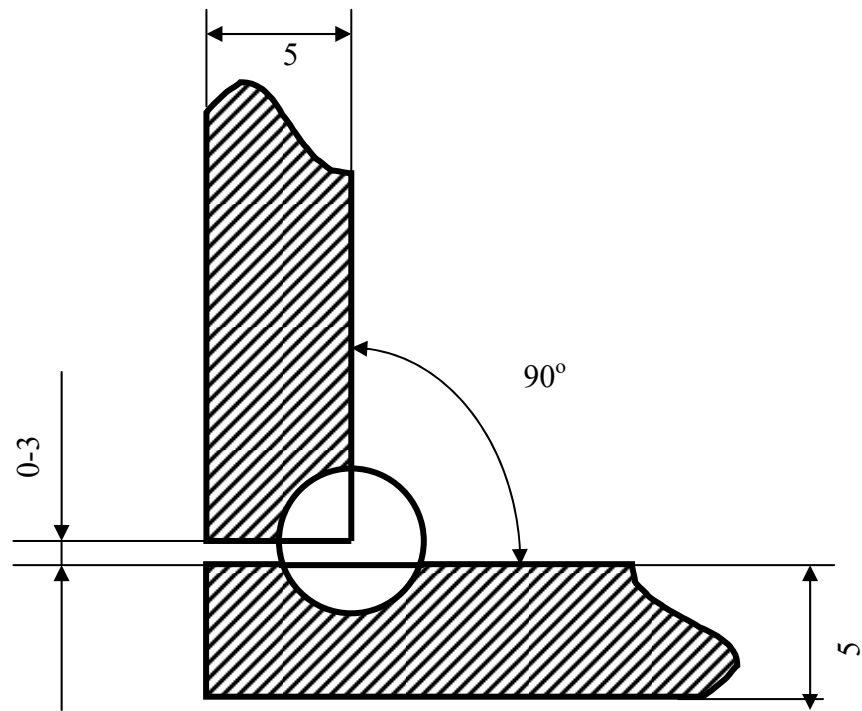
Схема розрахунку зварювального з'єднання
